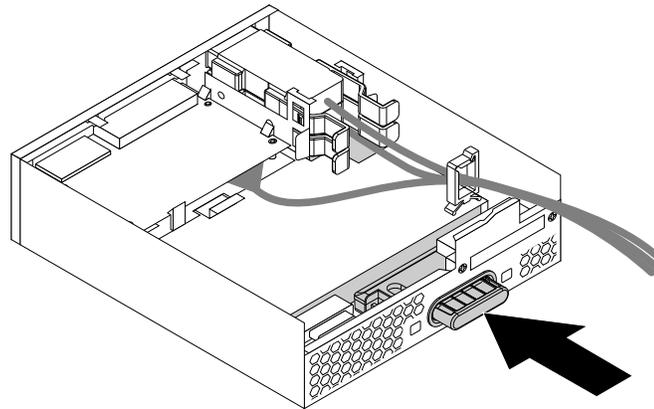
Das flache optische Laufwerk aus dem Flexmodul entfernen
